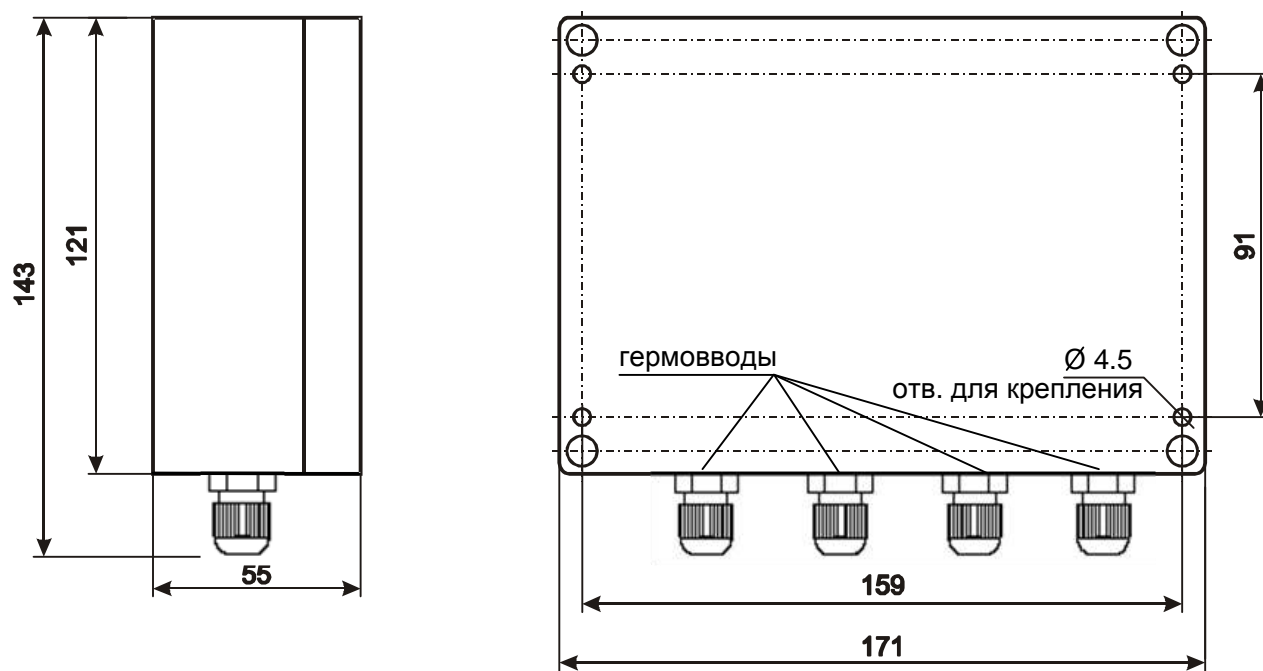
Внешний вид и габаритные размеры БРЛ в исп. IP65
